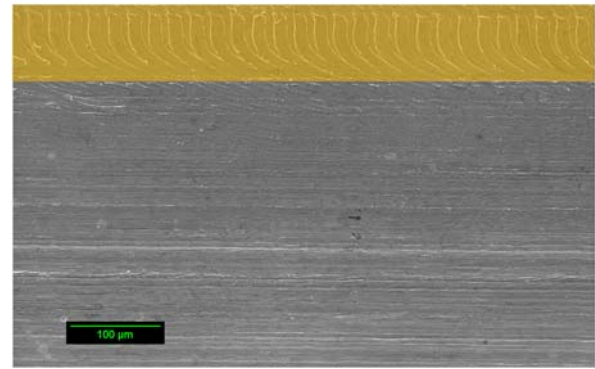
Ausschnitt aus einem gefrästen Kerbgrund (REM)
